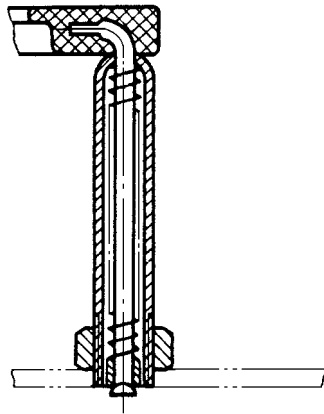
装配图中的圆柱螺旋弹簧示意画法(二)
